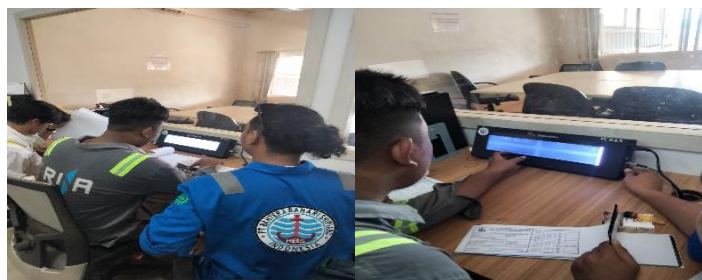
236. *Visual Welding Inspection Tank
